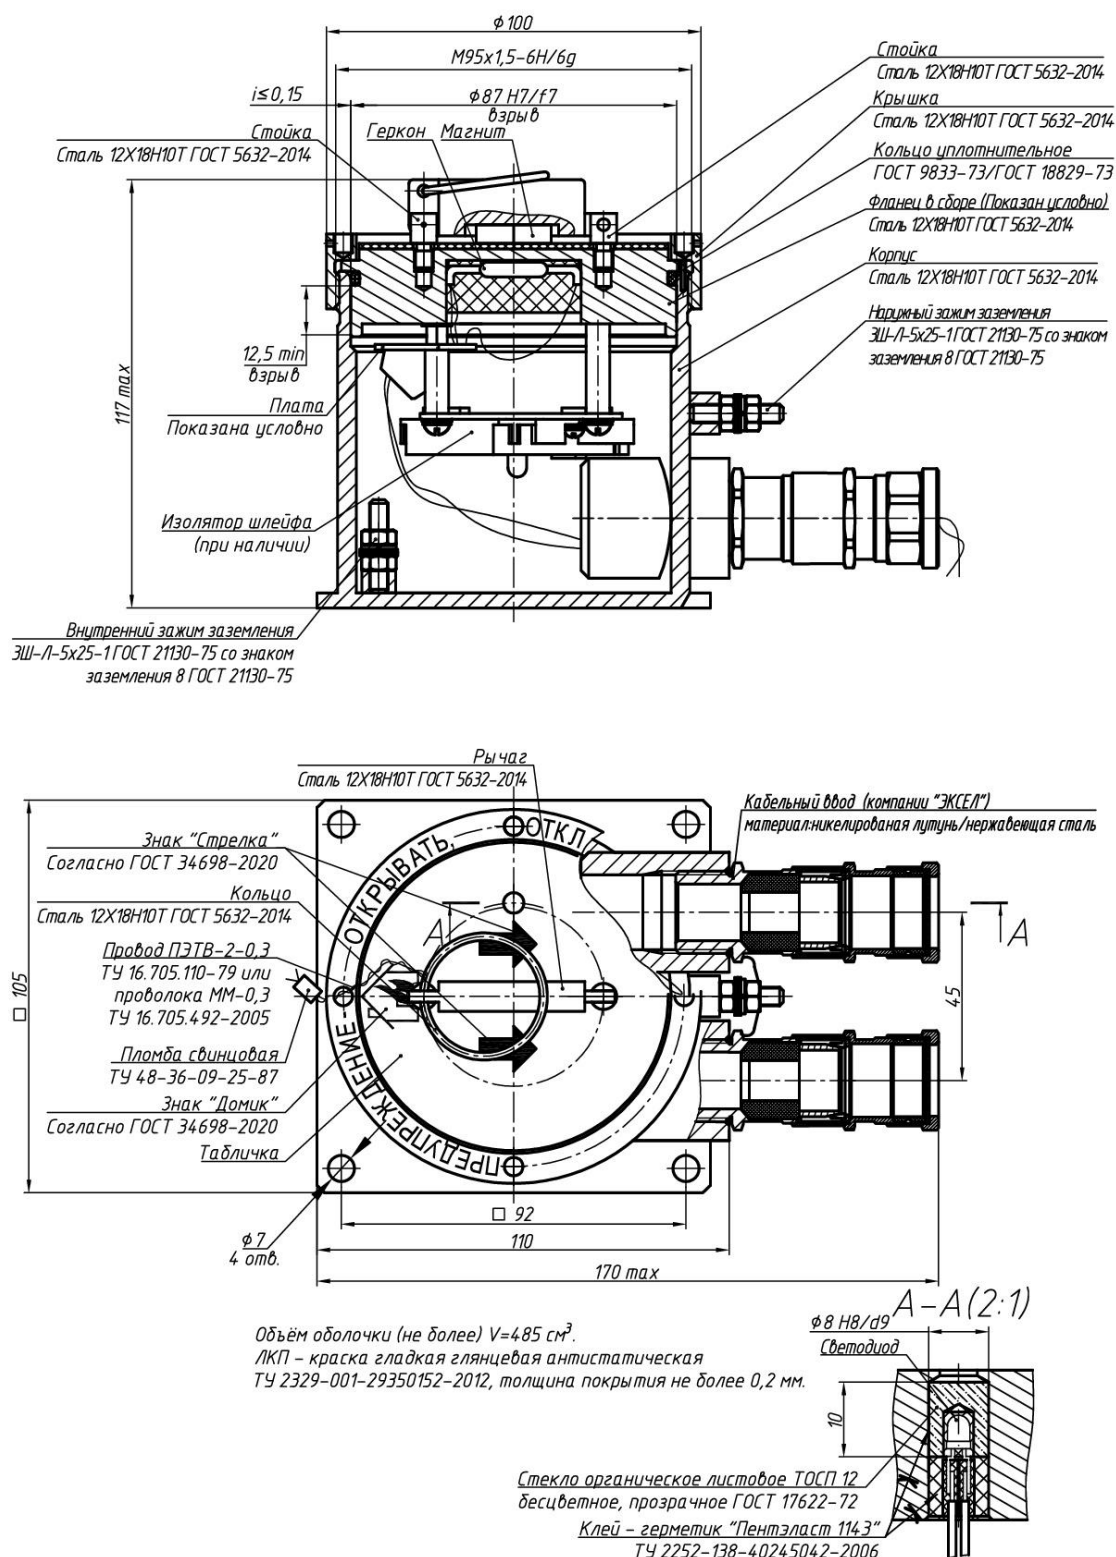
Габаритный чертёж взрывозащищённых устройств дистанционного пуска ЕхУДП-1-РЗ в корпусе из нержавеющей стали, совмещённый с чертежом взрывозащиты. Монтаж кабеля диаметром от 6 до 18 мм. Надписи и стрелки на табличке тёмного цвета, фон таблички белый. Маркировку смотри в п. 1.6.
